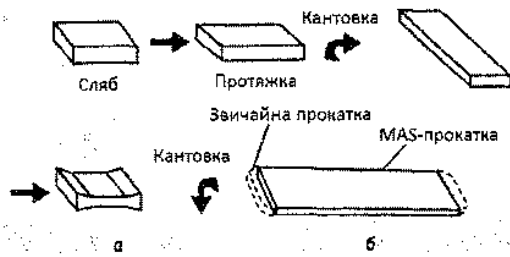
Принцип MAS-прокатки для зменшення торцевої обрізи: а — профіль по товщині після розбивки ширини; б — форма розкату в плані після прокатки до кінцевої ширини.
